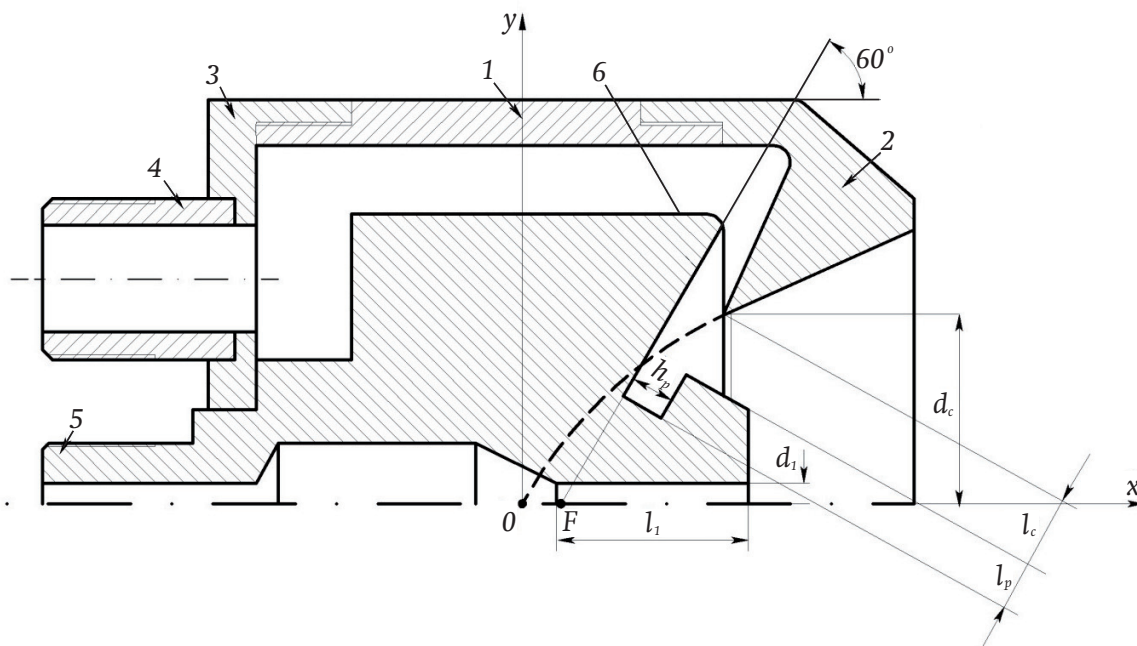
Конструктивная схема распылителя: 1 – корпус; 2 – резонаторная втулка; 3 – торцевая крышка; 4, 5 – штуцеры; 6 – центральное цилиндрическое тело
